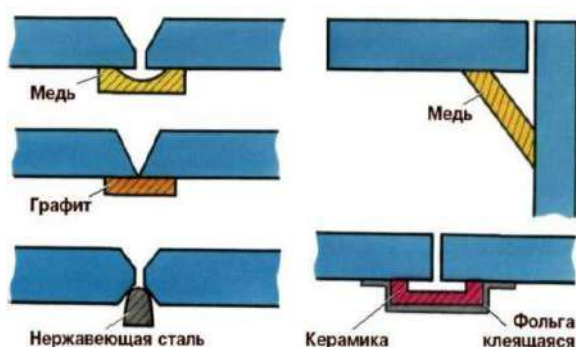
Подкладки для защиты от вытекания металла из сварочной ванны.
